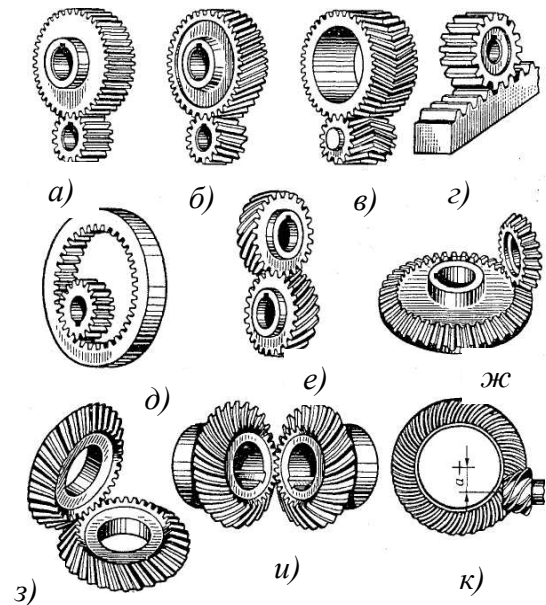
Виды зубчатых передач: а, б, в – цилиндрические зубчатые передачи с внешним зацеплением; г – реечная передача; д – цилиндрическая передача с внутренним зацеплением; е – зубчатая винтовая передача; ж, з, и – конические зубчатые передачи; к – гипоидная передача
